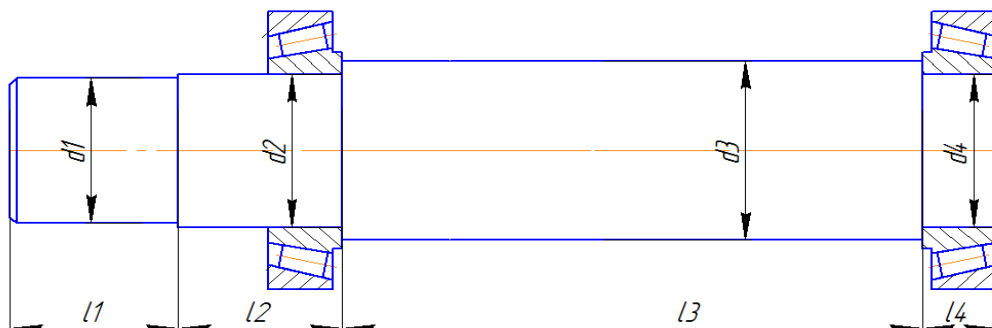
Проектный расчет тихоходного вала конического редуктора
